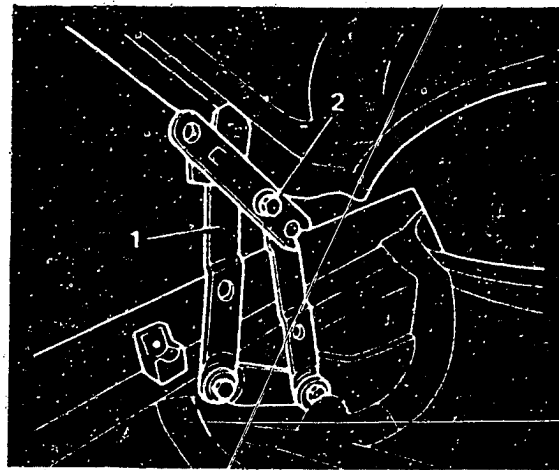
Der Scherenmechanismus der Motorhaubenbefestigung (1) mit der praktischen Zentrierschraube (2).
